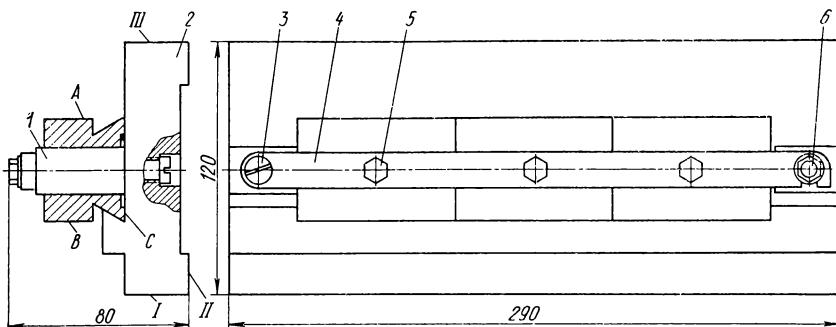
Приспособление для шлифования боковых сторон призматических резцов:
